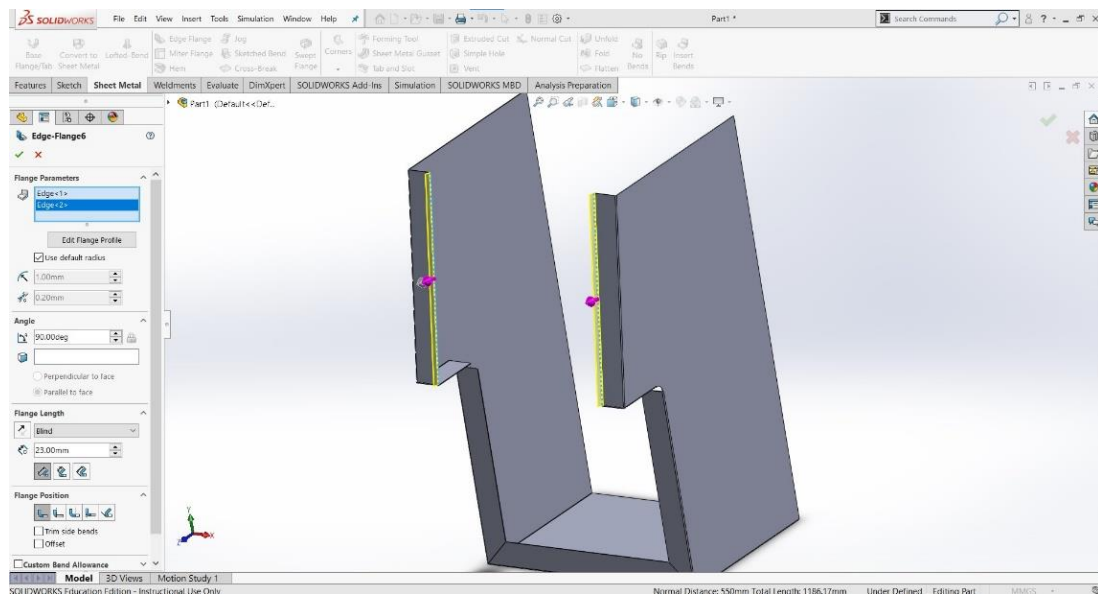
Oblikovanje dijelova baze komponente za postavljanje prednje ploče
